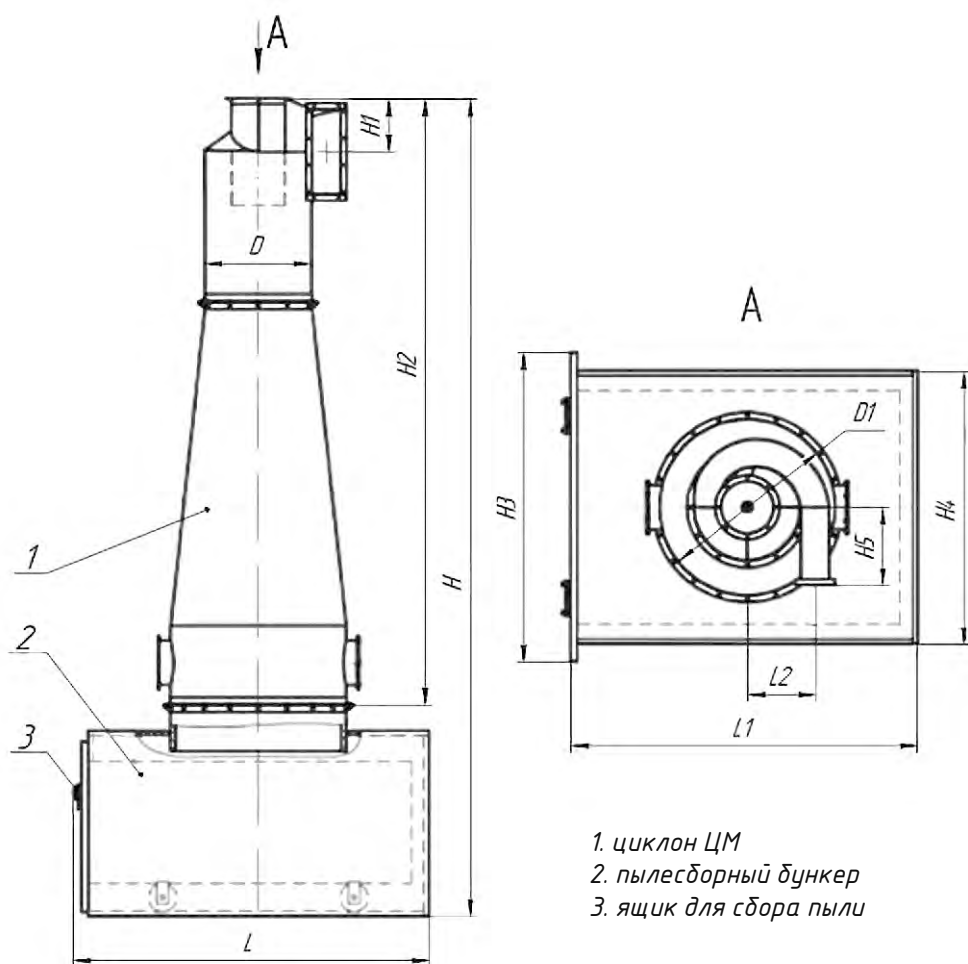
Габаритные и присоединительные размеры циклонов ЦМ на пылесборнике.
